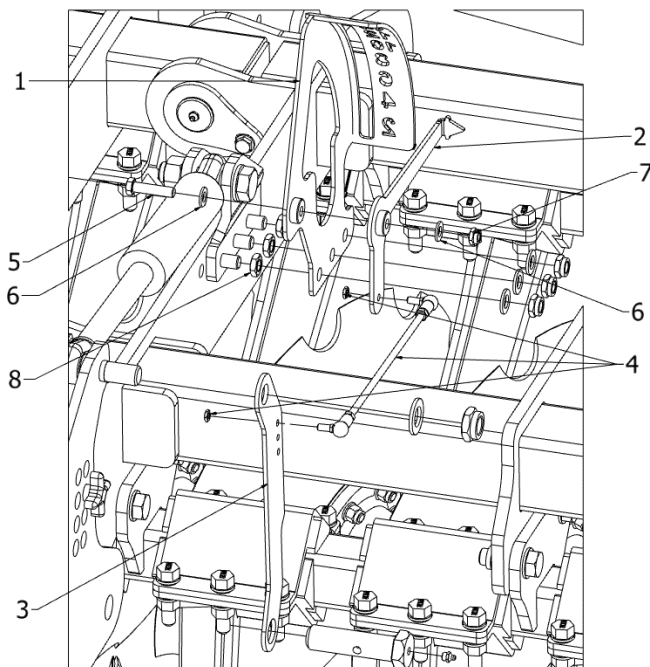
Befestigung des Zylinderohrs für die Wellenverstellung am Maschinenrahmen.
